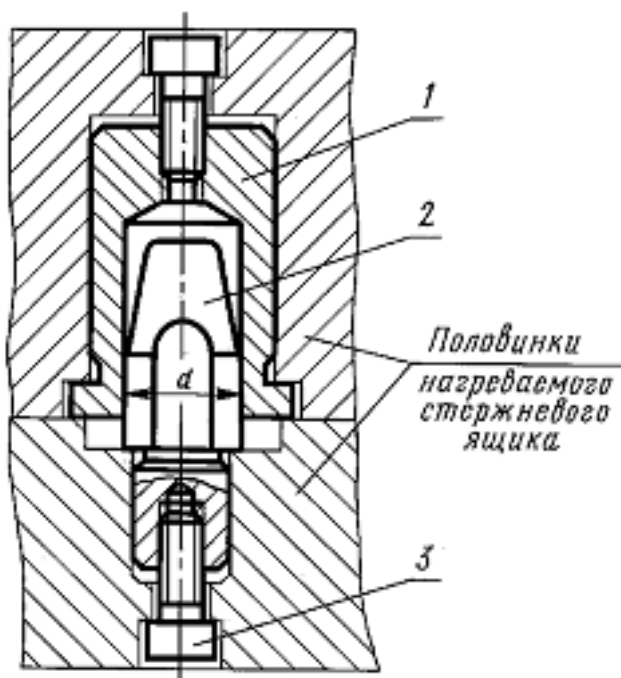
Конструкция центрирующего соединения с винтовым креплением
